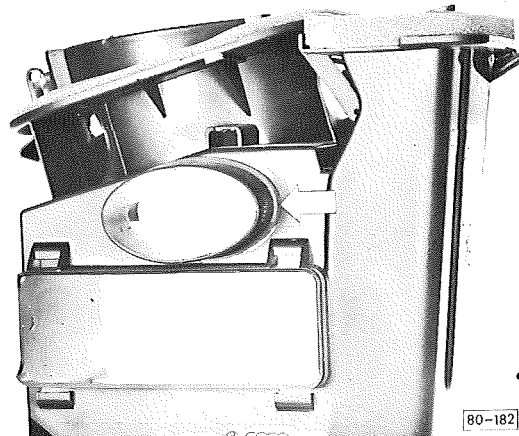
Désassemblage et assemblage du caisson d'air frais
